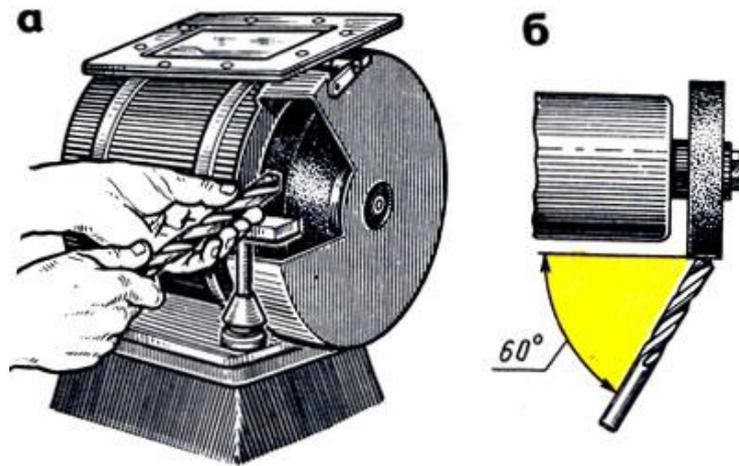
Заточка сверла: а - положение сверла в руках, б - положение сверла относительно шлифовального круга
